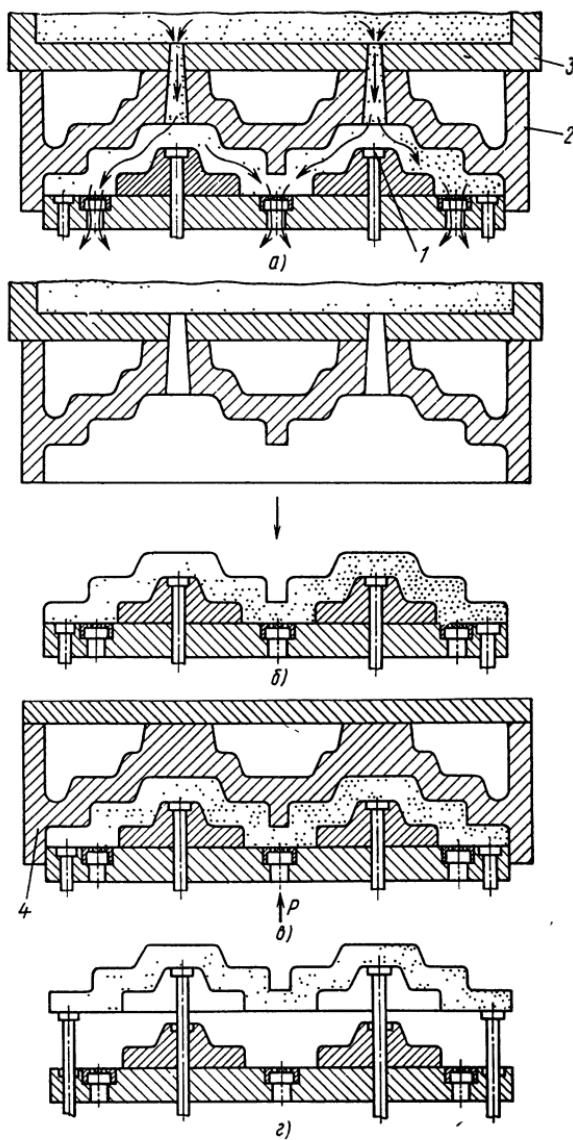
Схема пескодувно-прессового метода изготовления оболочковых полуформ
